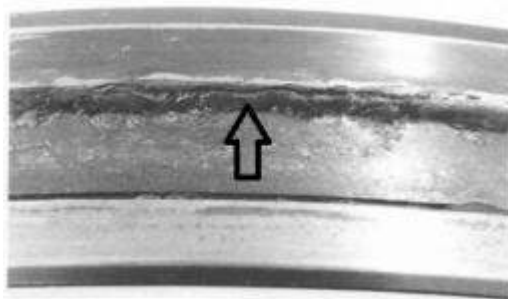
Заедание по торцу борта внутреннего кольца подшипника типоразмера 2002834
